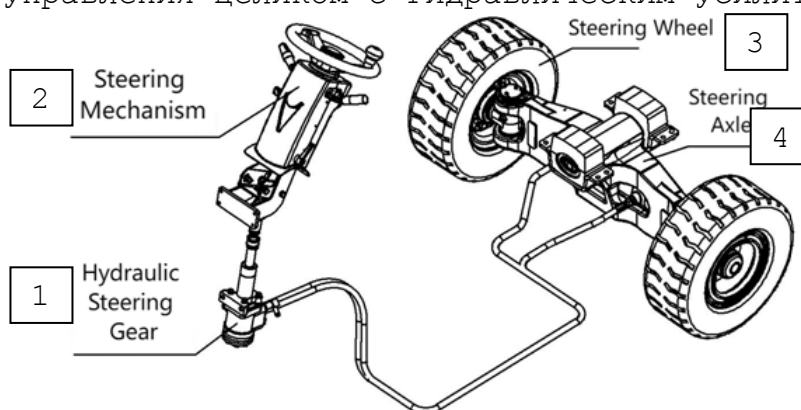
Схема конструкции рулевого управления вилочного погрузчика:
